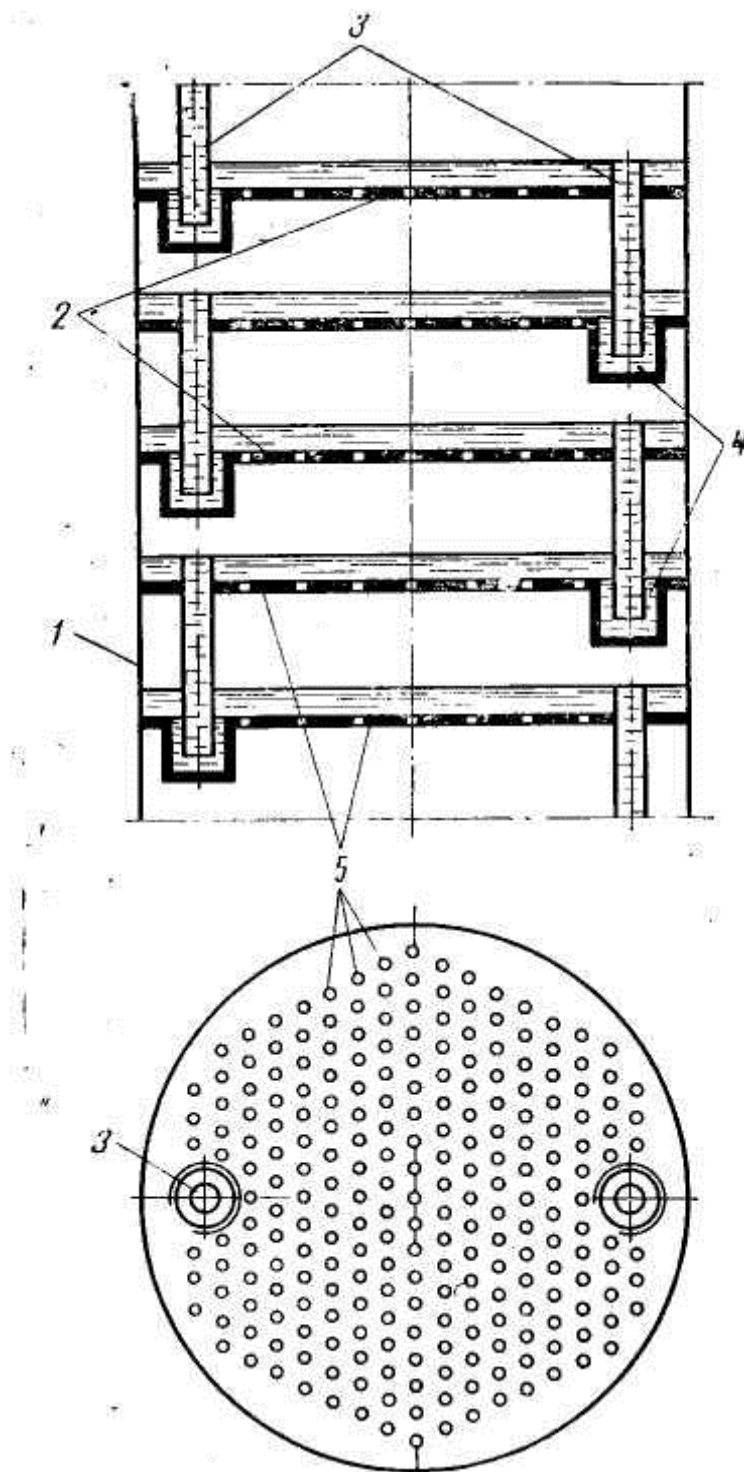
Пристрій сітчаті тарілки: / - корпус колони; 2 - тарілка; 3 зливна труба; 4 гідравлічний затвор; 5 – отвори
